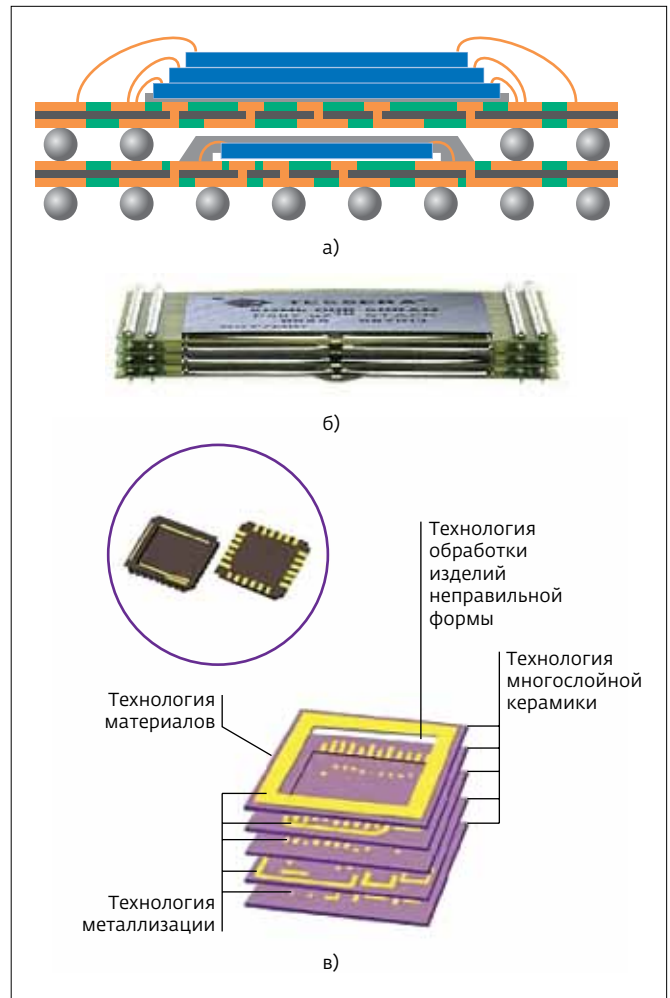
Примеры многокристалльного корпуса PoP (а), четырехуровневой стековой сборки СОЗУ (б), металлокерамического многокристалльного корпуса типа QFN (в) (источник Tessaera)
